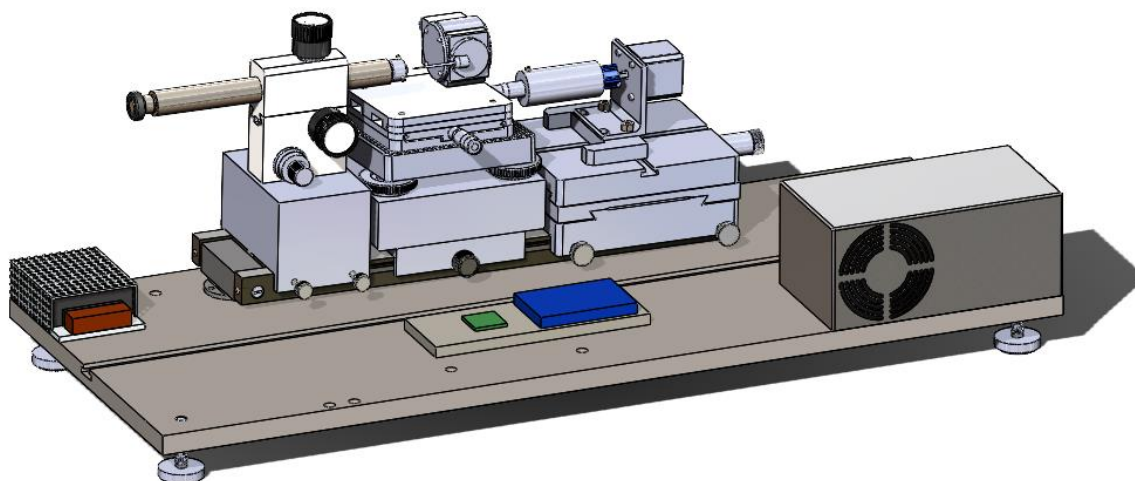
Устройство для микрошлифовальной обработки твердосплавных фильер
